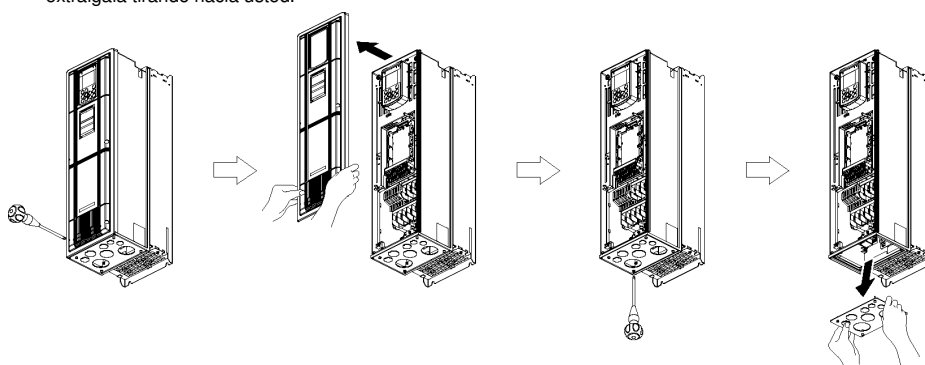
Extracción de la placa frontal y de la placa del cableado (FRN37AQ1M-4□)
